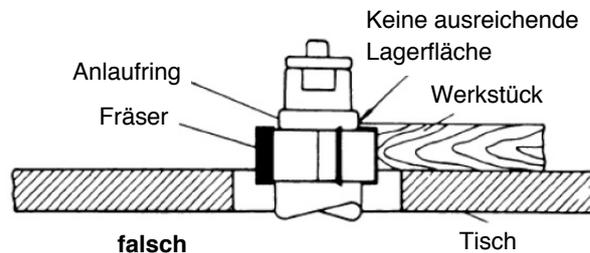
Fräsen mit Anlaufring ohne ausreichende Anlauffläche
